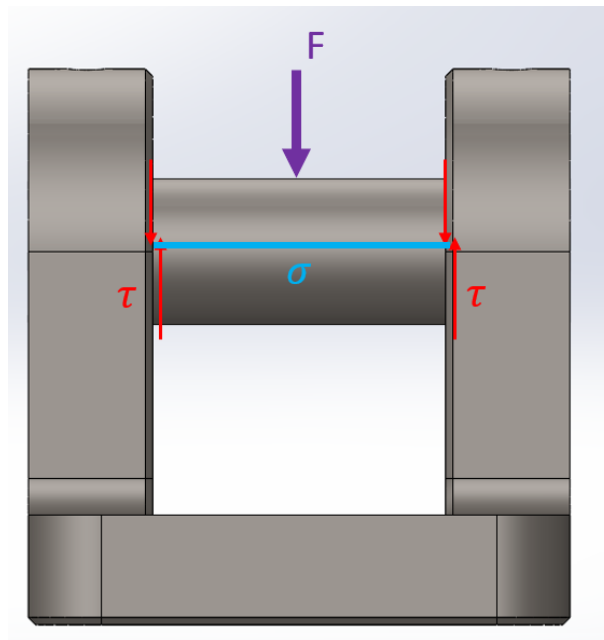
DCL de fuerzas y esfuerzos en el eje de rodamientos
